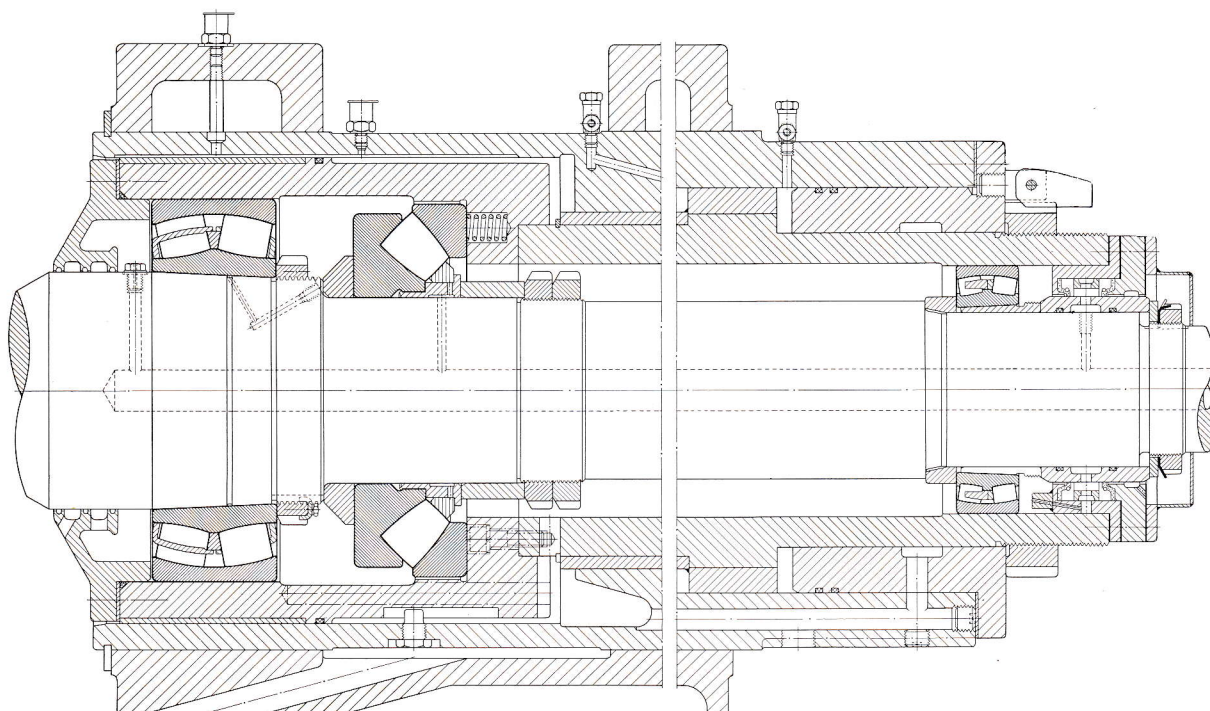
Disposición de rodamientos del eje de una refinadora de muelas con alta presión de moler
